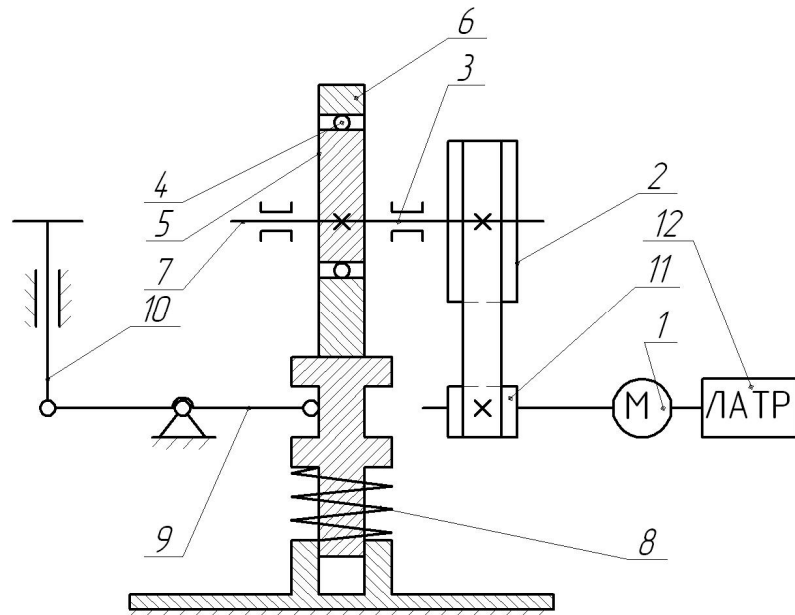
Кінематична схема лабораторної установки механізму хитання кристаллизатора
